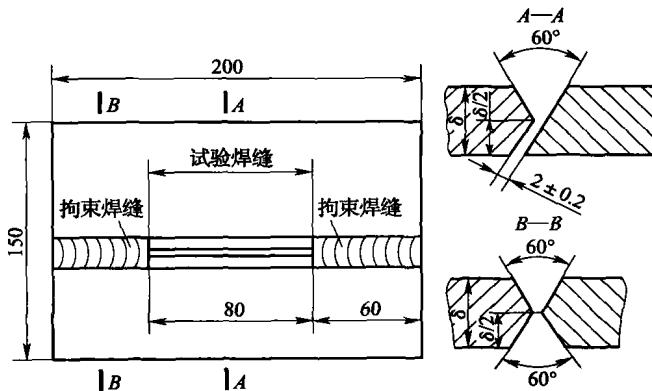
2—1 斜 Y 形坡口焊接裂纹试验用试件形状及尺寸
